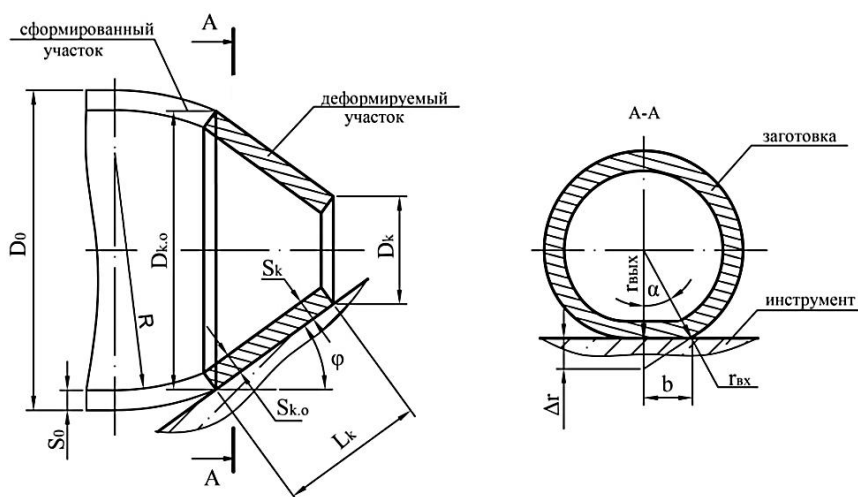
Схема обжатий очага деформации при обкатывании дна
